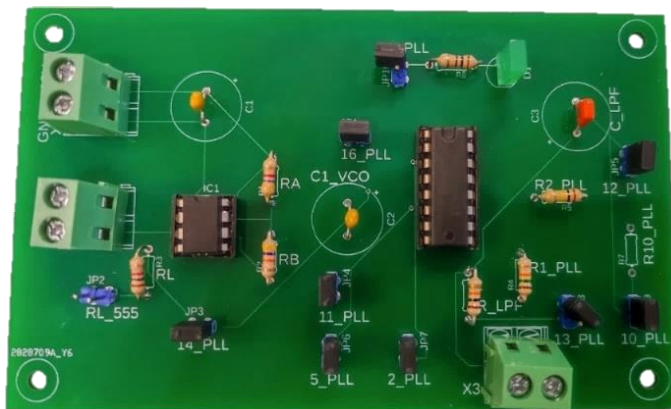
Imatge de la placa PCB dissenyada pel prototip.
